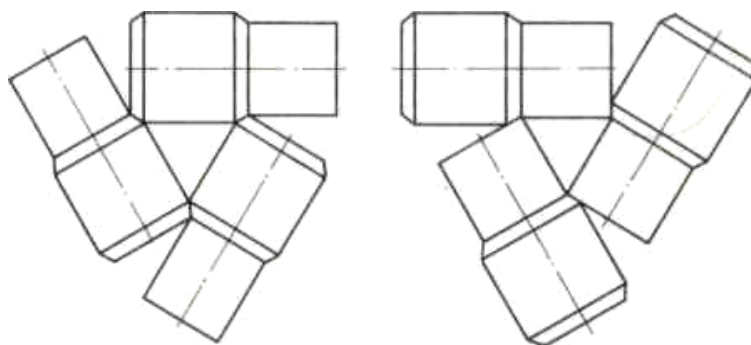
Сборка трехвалковых калибров с размещением двух ручьев на бочке каждого валка
